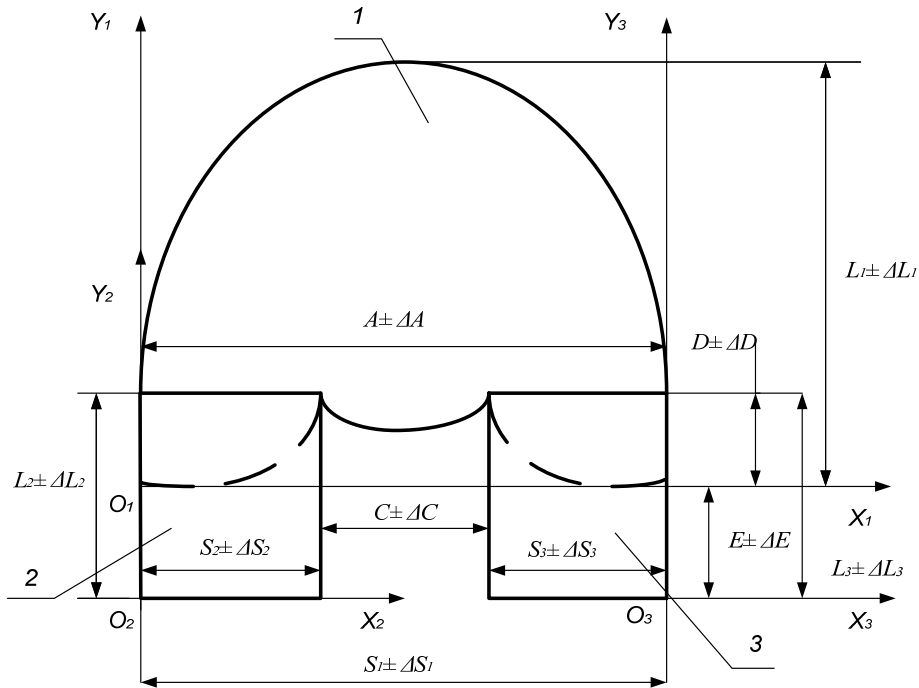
Базування деталей верху взуття із системою відліку з кута деталі, відлік координат з правого кута третьої деталі: 1 – базова деталь; 2 – друга деталь; 3 – третя деталь.
